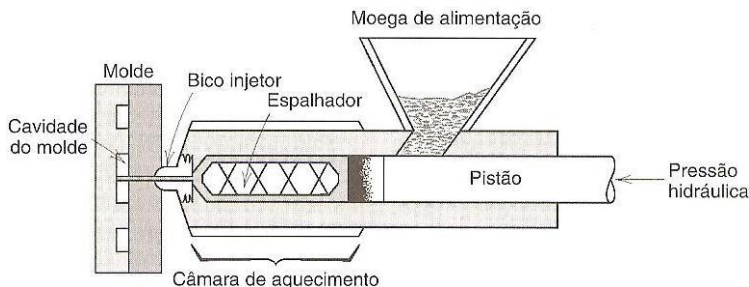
Esquema de um equipamento para moldagem por injeção. Fonte: CALLISTER, 2002, p. 347.
